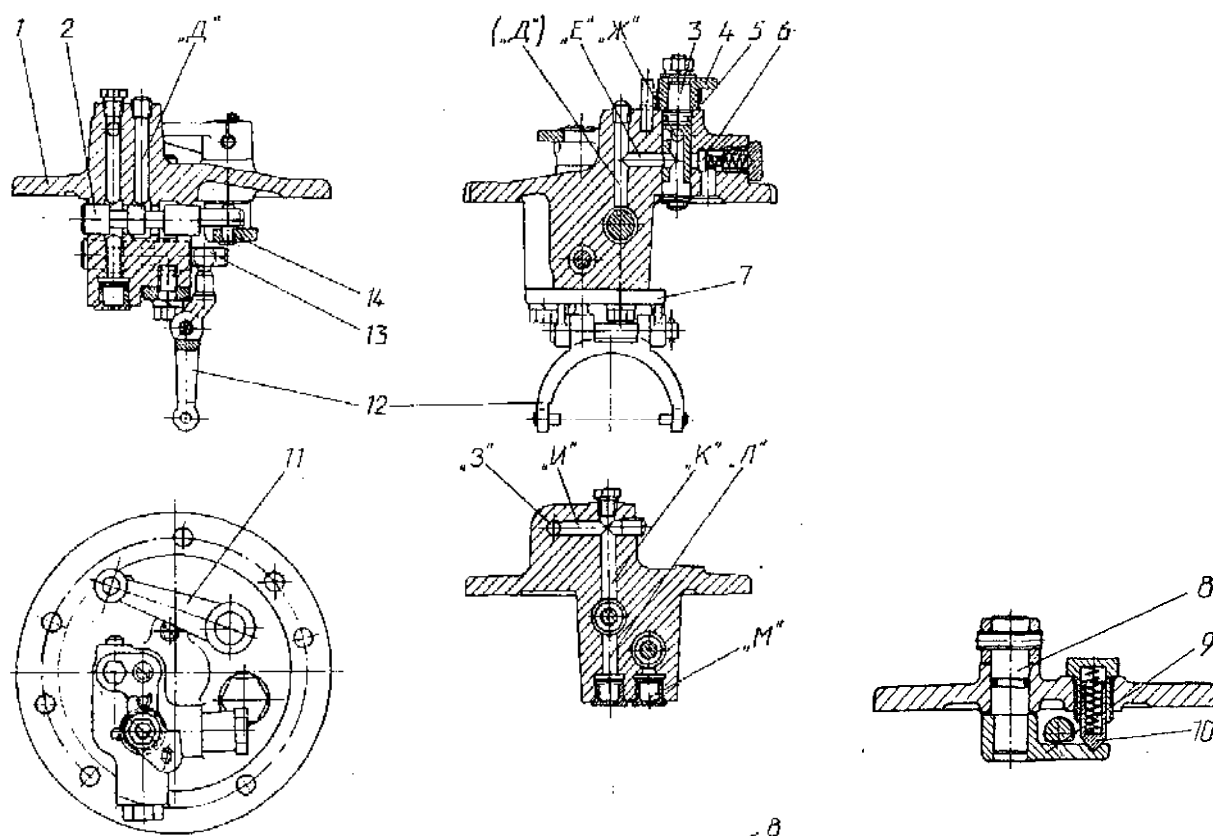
Кран управління ПВМ: 1 - корпус; 2, 3, 13 - деталі золотника; 4, 9, 11 - деталі важеля; 5 - пружина; 6 - клапан; 7 - кронштейн; 8 - вісь; 10 -
